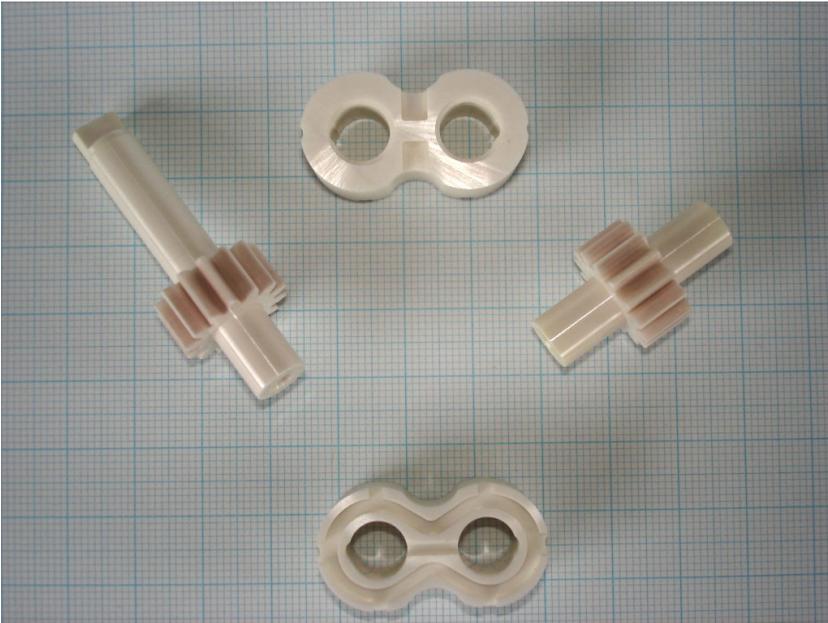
Bauteile einer Zahnradgruppe für Pumpe aus ZrO_2 Y-TZP
